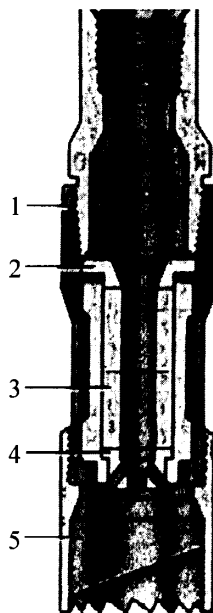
Магнитный фрезер: 1 – корпус; 2 – верхний полюс; 3 – магнит; 4 – нижний полюс; 5 – колонка
